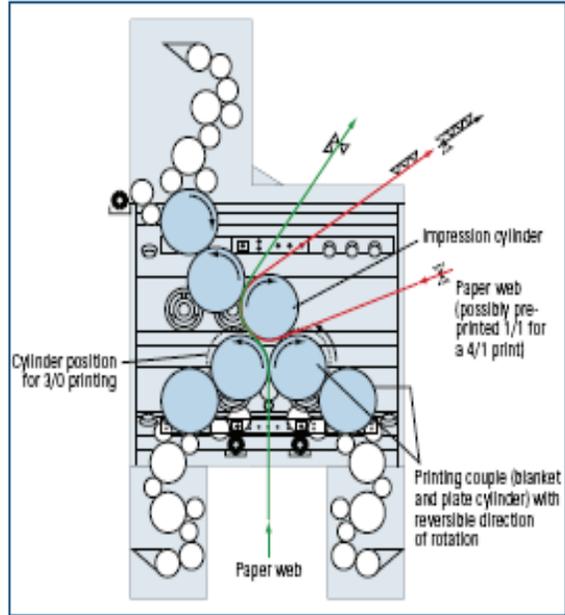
Konstruksi unit pencetakan blanket to
